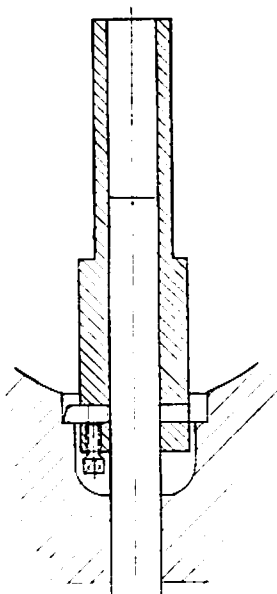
Bohrwerkzeug zum Nachdrehen der Ventilsitzausnehmung.
